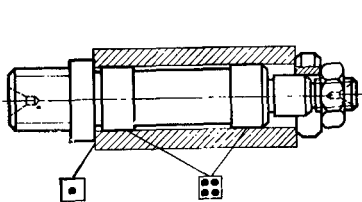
Схема базирования заготовок на жесткой оправке по отверстию (двойная направляющая база) и торцу (опорная база)
